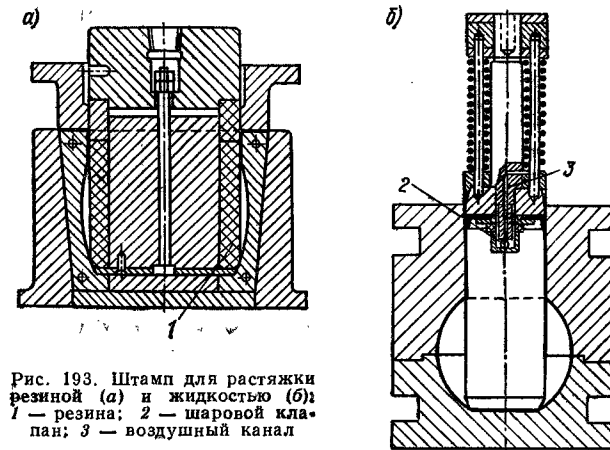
Штамп для растяжки резиной (а) и жидкостью (б): 1 — резина; 2 — шаровой клапан; 3 — воздушный канал
